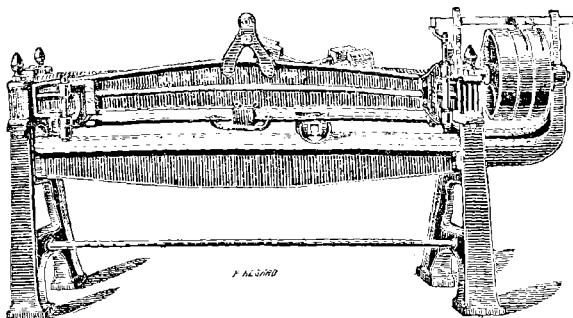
Machine à cylindrer les cuirs, de Tourin.
